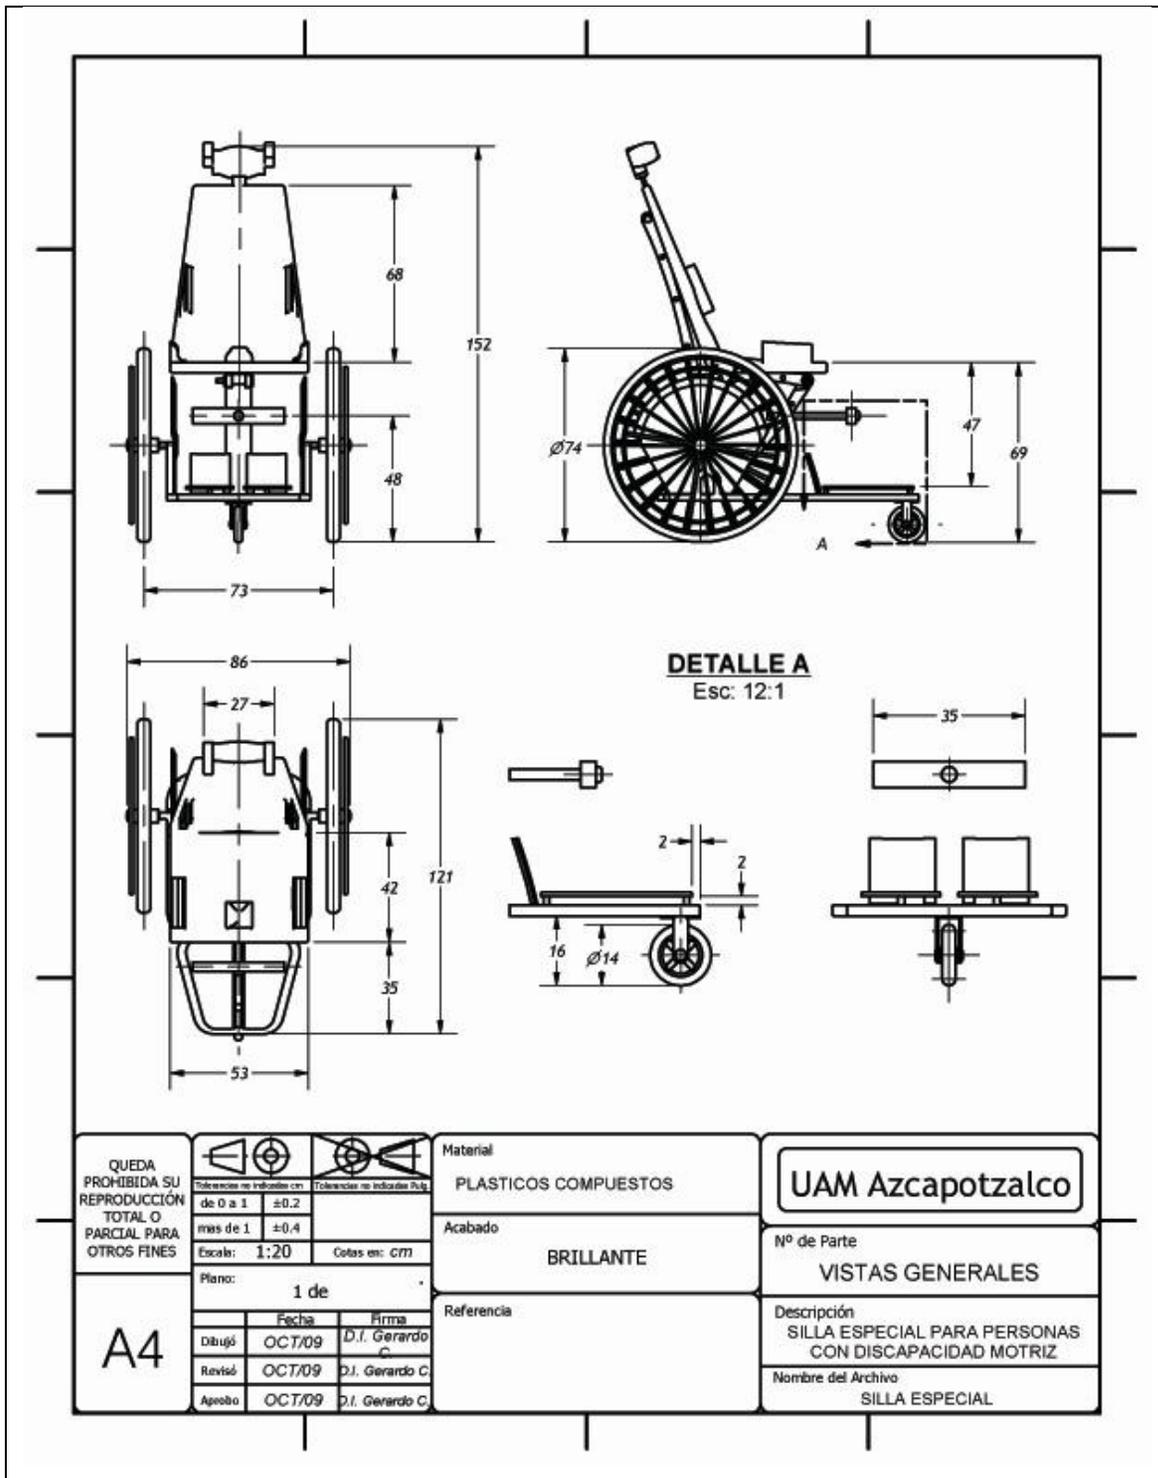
Planos de producción: vistas generales. Propuesta del Autor.
